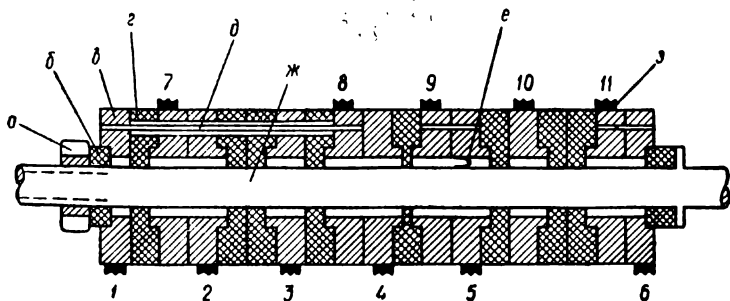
Горизонтальный осевой разрез цилиндра УРК
